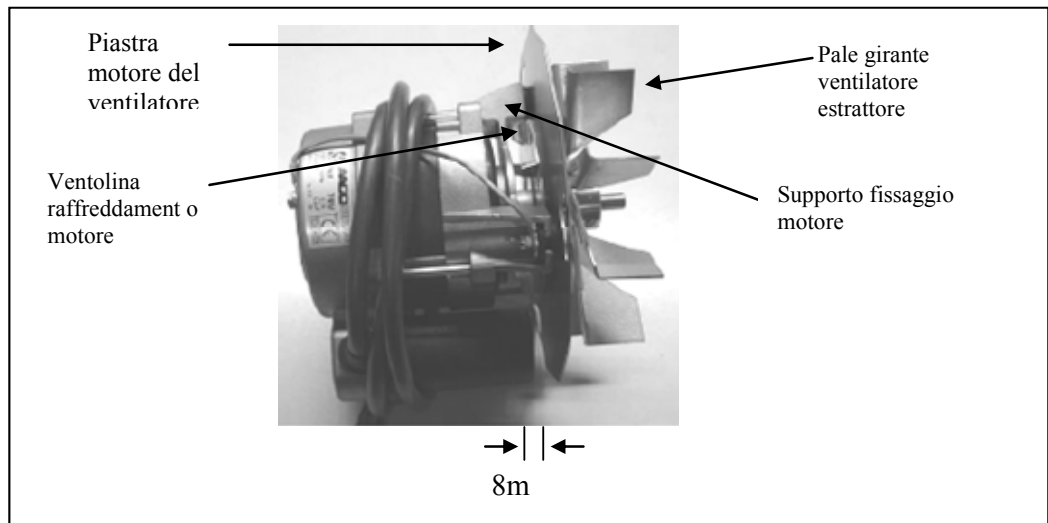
Posizione delle pale del ventilatore estrattore sull'asse (senso di rotazione: in senso anti-orario visto dall'estremità dell'asse)
